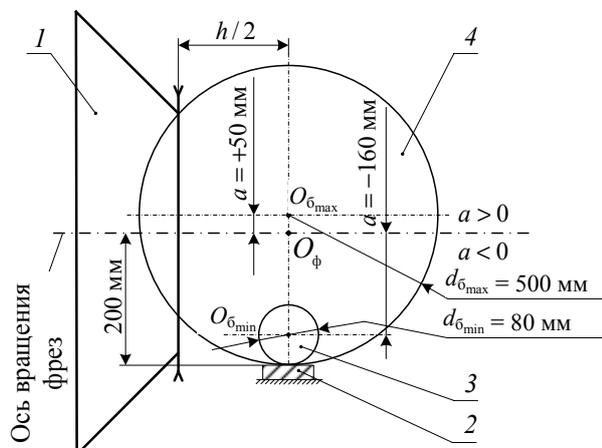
Схема обработки бревен на фрезерно-брусующем станке PSP 500 (SAB, Германия):
